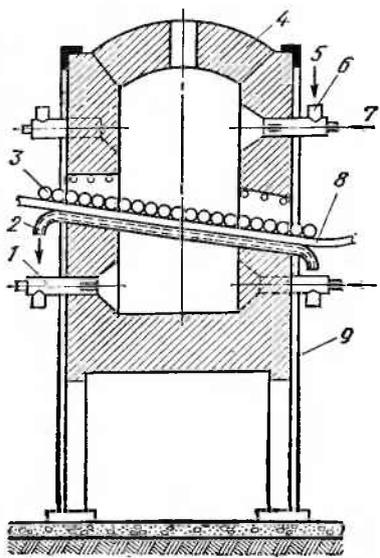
Печь для скоростного нагрева цилиндрических заготовок
